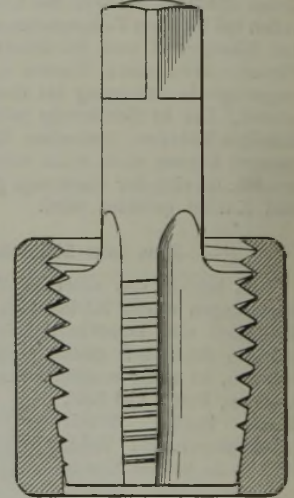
Gewindebohrer mit Flankenschnitt für American Standard Taper Pipe, Briggs-Rohrgewinde.
